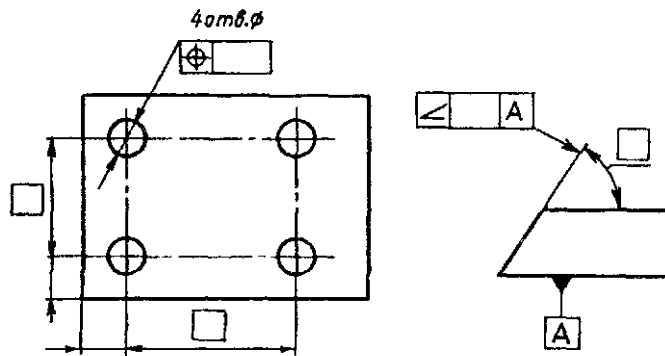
Нанесение номинальных линейных и угловых размеров при назначении допуска формы или расположения поверхностей
